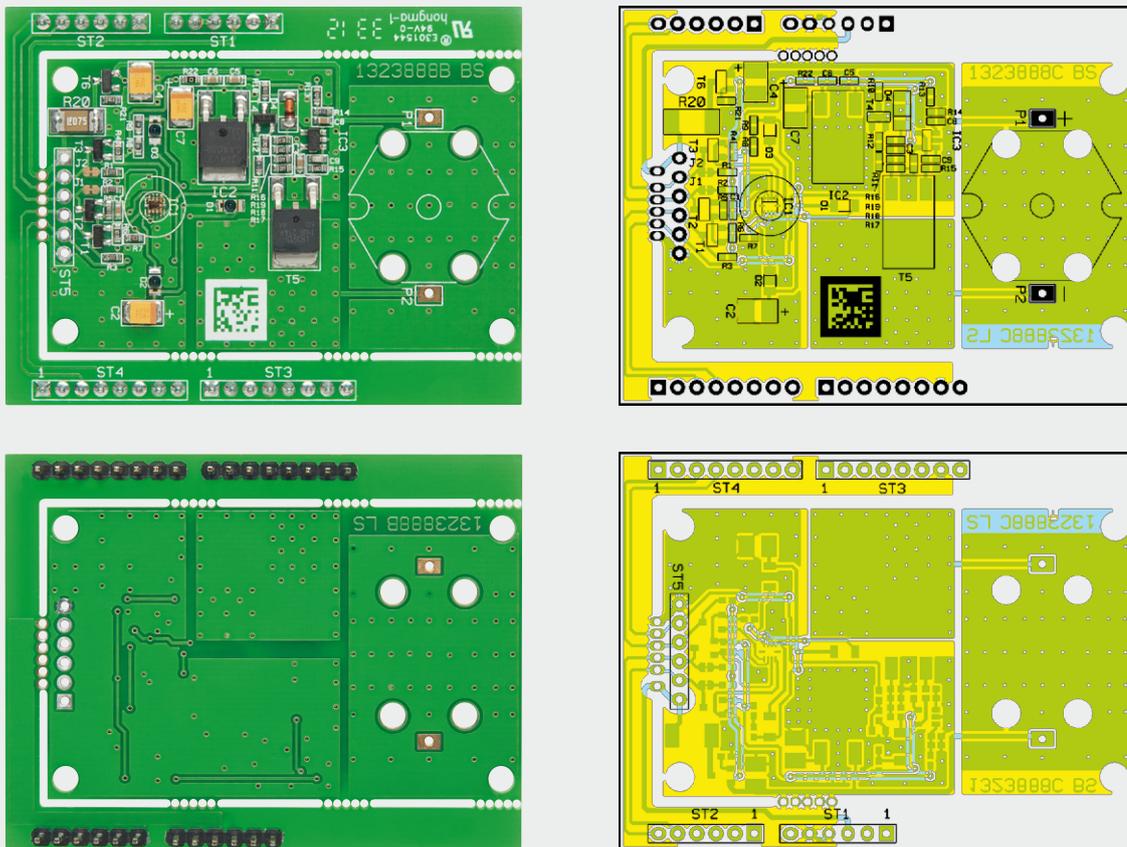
Ansicht der komplett bestückten Platine mit zugehörigem Bestückungsplan
